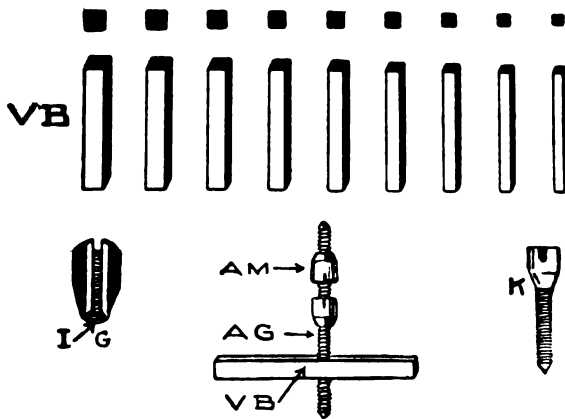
Verankerungsbalken (VB) in verschiedenen Größen mit eingelassenem Schraubengewinde, die durch einfaches Anlöten oder Mitgießen an die fixen Brückenteile eine Entlastung der Schraubenspindel bewirken. (IG) Innengewinde der Befestigungsmutter (AG), Außengewinde der Schraubenspindel (AM), die abgesetzte Mutter (K), Kopfschraube.
